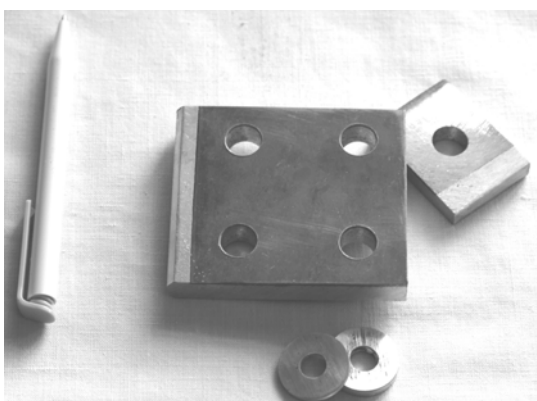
Переходные пластины (вверху) и промежуточные шайбы (внизу), изготовленные из биметалла медь-алюминий
